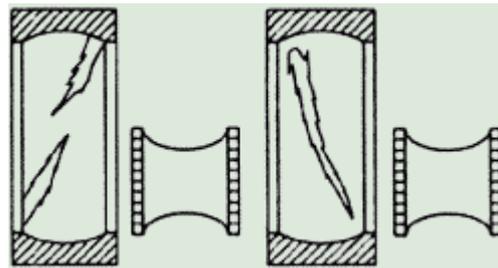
Повреждения подшипника из-за несоосности колец: а) несоосность внешнего кольца относительно вала; б) несоосность вала относительно корпуса подшипника.
